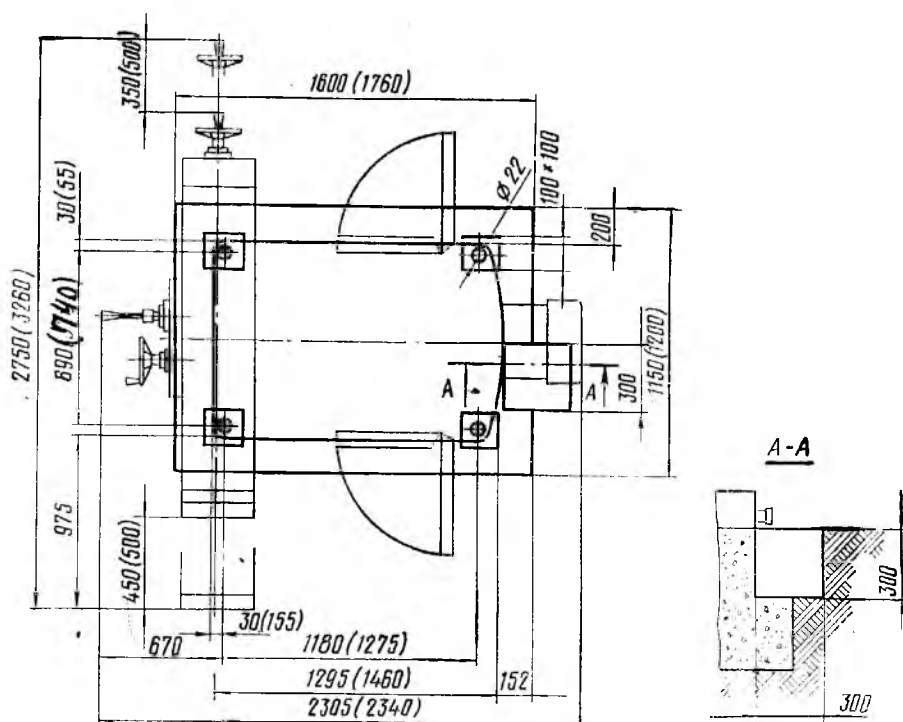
Установочный чертеж станков 6P12 (6P13)
